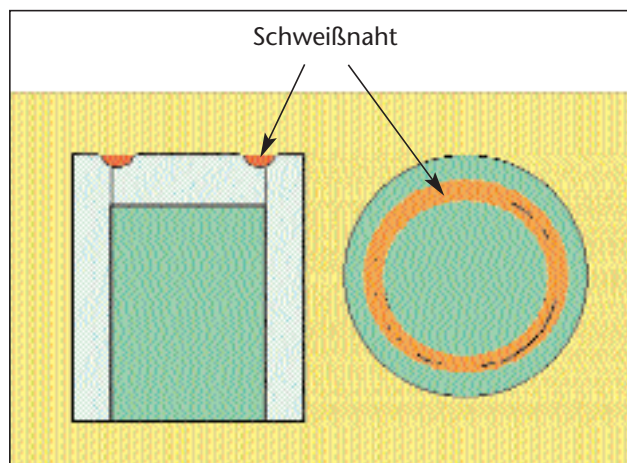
Rohr mit eingeschweisster Deckplatte
